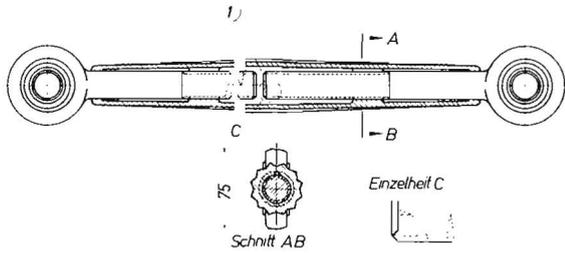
Oberlenker mit Kugelgelenkanschlüssen
